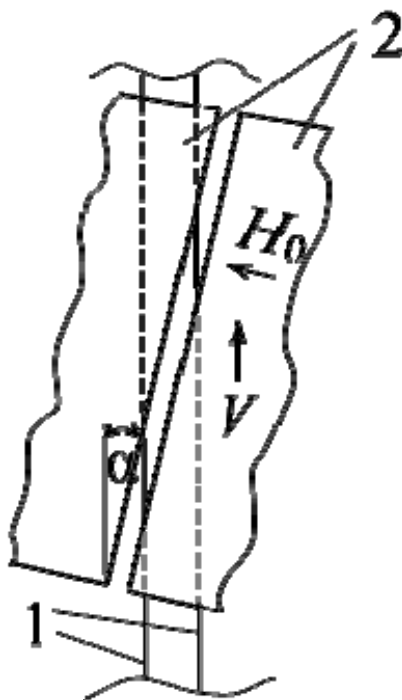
Расположение КМИ при осуществлении способа намагничивания [4]: 1 – контролируемый сварной шов; 2 – пластины прямоугольного сечения
